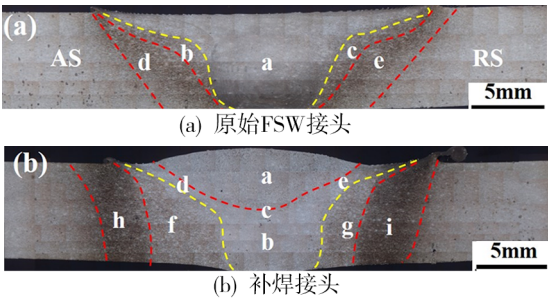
原始 FSW 接头与补焊接头截面形貌
